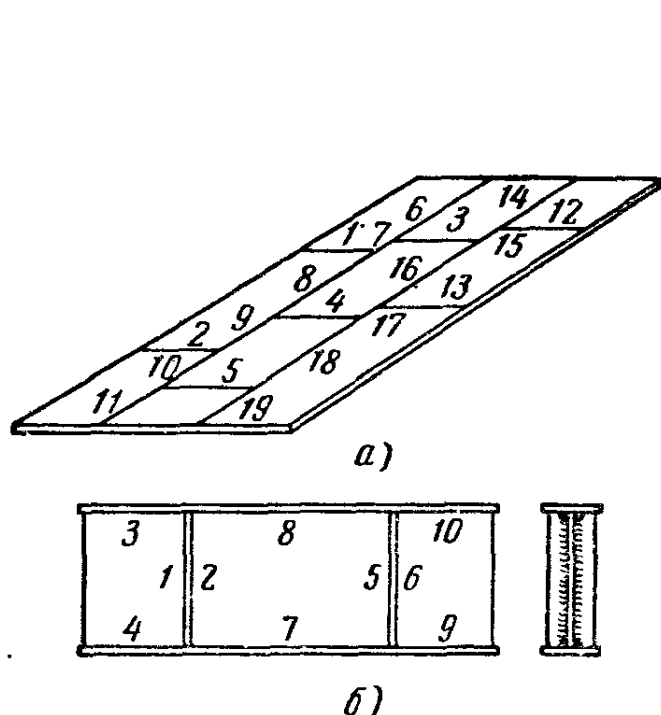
Правильная последовательность наложения швов при сварке листов: а—настила, б—двухтавровой балки
